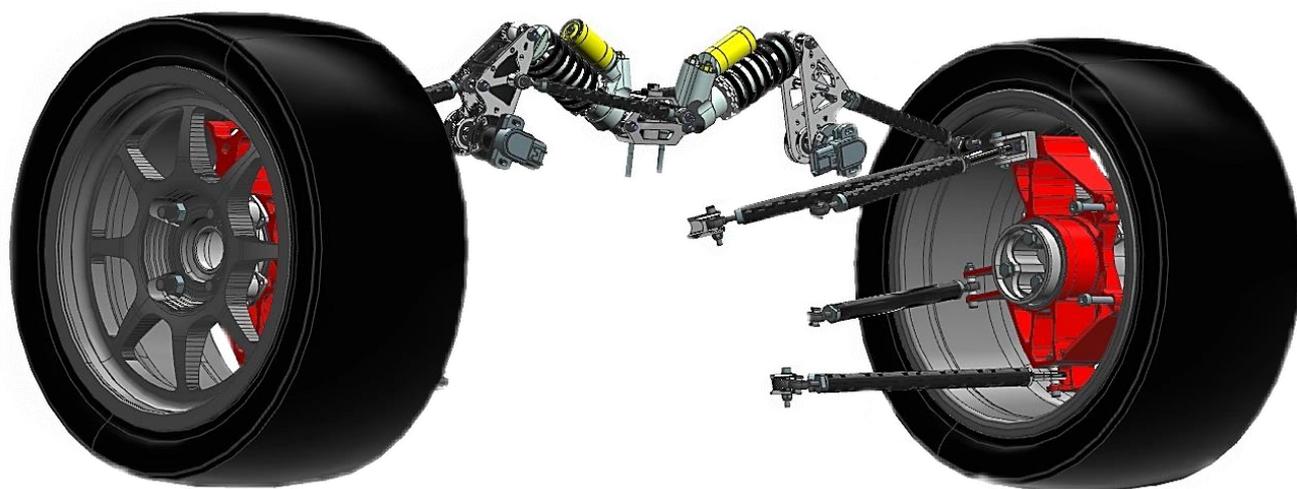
Конструкция передней подвески с системой push-rod на верхний рычаг
